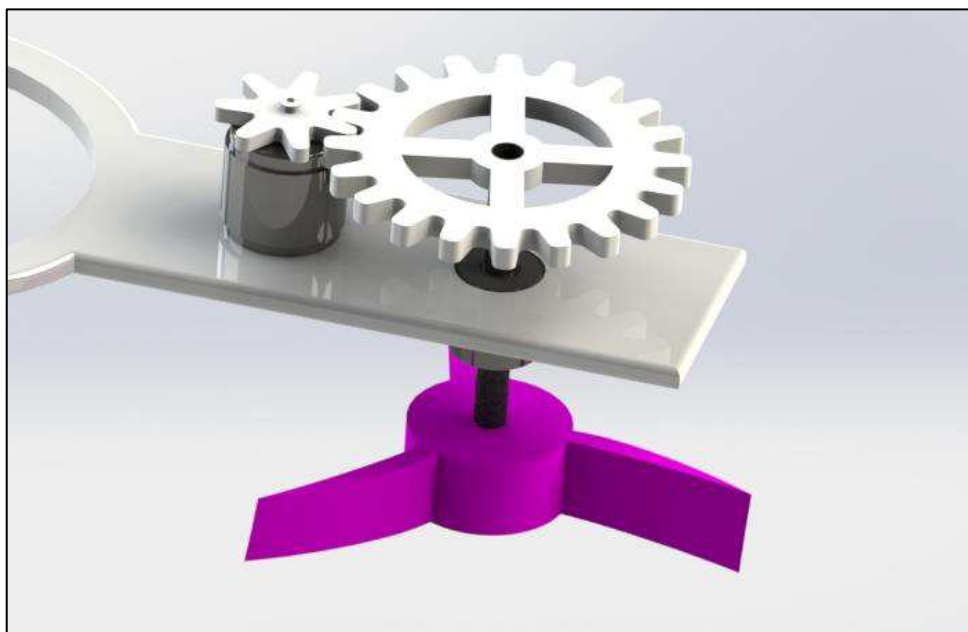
Mecanismo de transmissão de rotação com uso de engrenagens.
